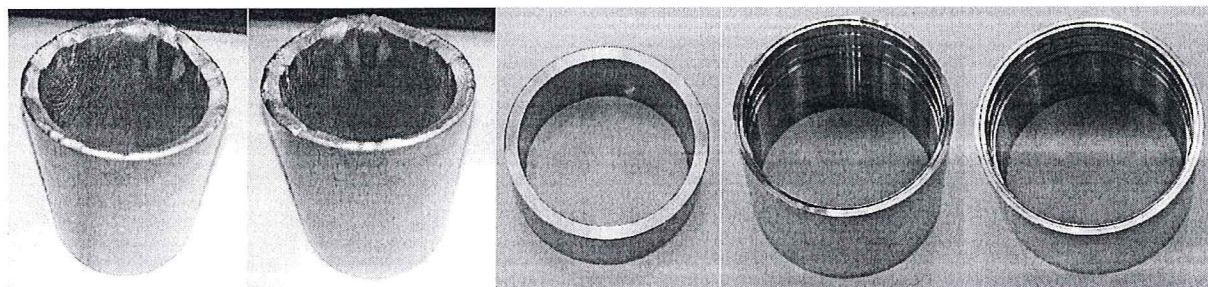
Стаканы после третьей вытяжки, заготовка – трубка и заготовки экранов.
